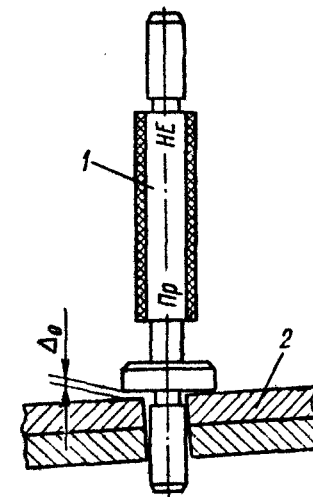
Контроль отверстия калибром-пробкой:
